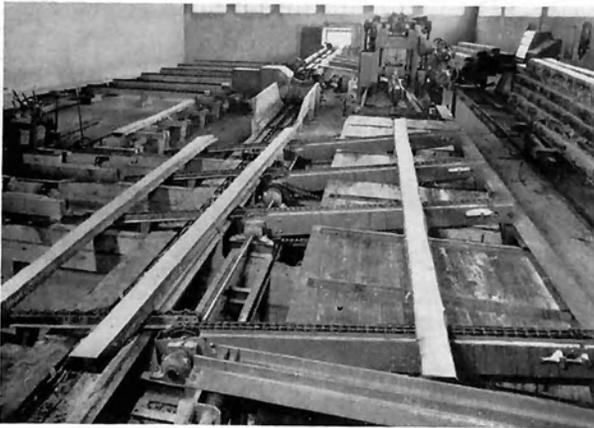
Rollschienen und Rollenbahnen für Prismen („langes, schmales Fördergut“) in einem Sägewerk. Die auf einer Rollenbahn vom Vorschnittgatter kommenden Prismen werden durch einen aus der Rollenbahn hebbaren Mehrfachkettenförderer – dessen Antrieb durch den im Vordergrund sichtbaren Anschlag eingeschaltet wird – über Rollschienen nach links zum Nachschnittgatter transportiert; die Seitenware läuft, während das Prisma noch im Gatter gehalten wird, über die Rollenbahn – unter dem Anschlag durch – zu den Kappsägen und dem Doppelsäumer
